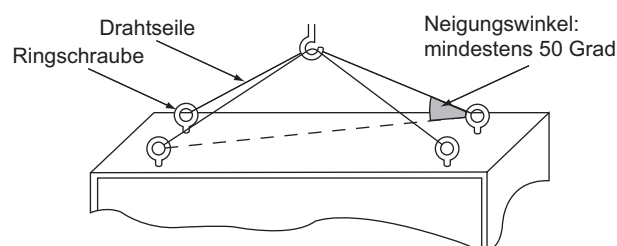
Schwebezustand beim Anheben mit Drahtseilen
